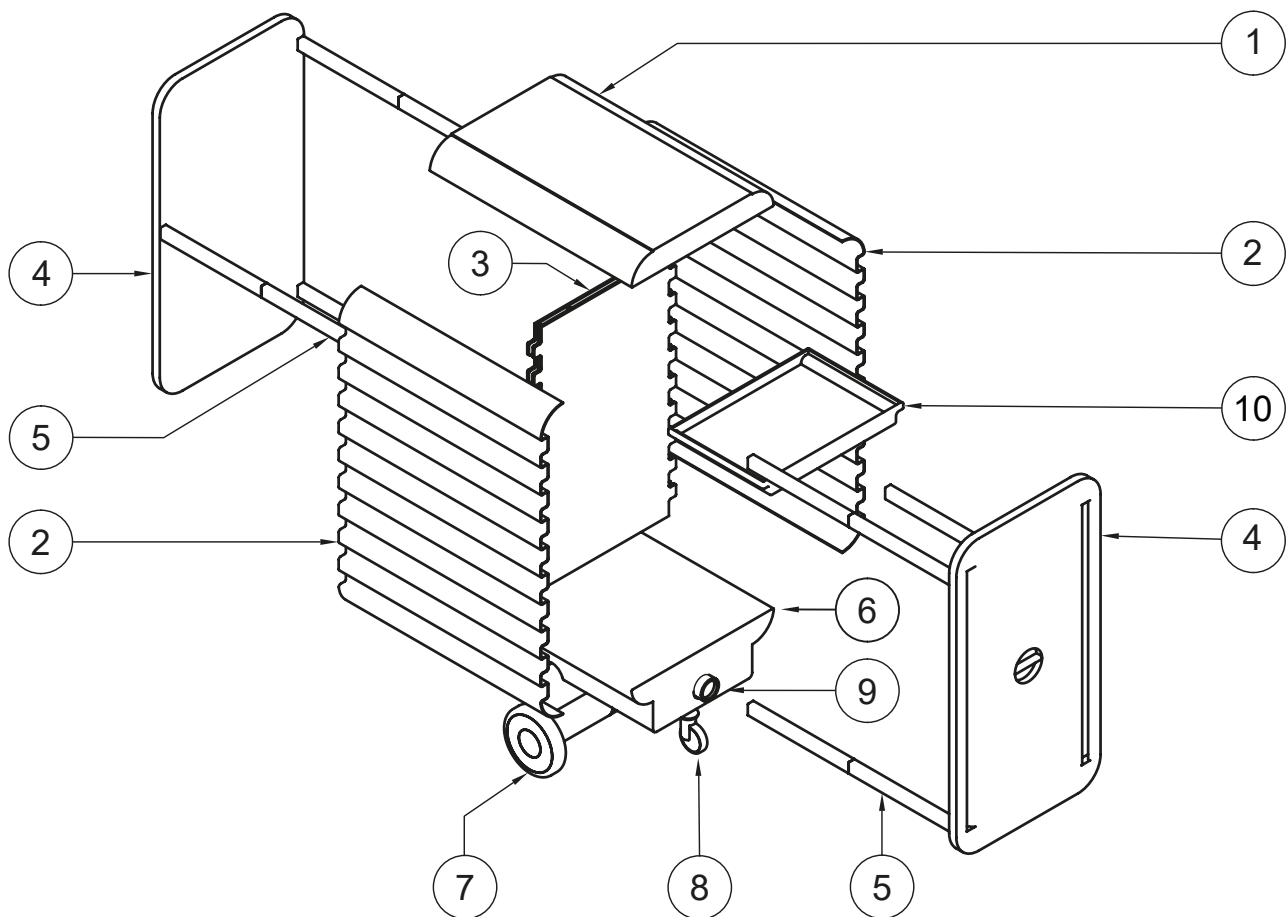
Vista explodida demonstradora dos componentes que constituem o P2Cv. Fonte: Autor.
